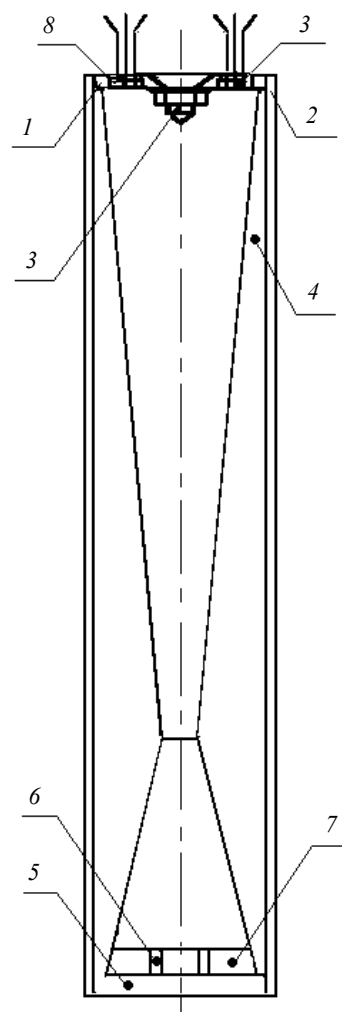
Схема тепловой трубы: 1 — верхняя крышка; 2 — цилиндрический корпус ТТ; 3 — конический турбулизатор; 4 — капиллярно-пористая вставка; 5 — нижняя крышка; 6 — инжекторные каналы; 7 — капиллярно-пористый испаритель; 8, 9 — емкостные датчики конденсации, измеряющие толщину слоя жидкого конденсата
